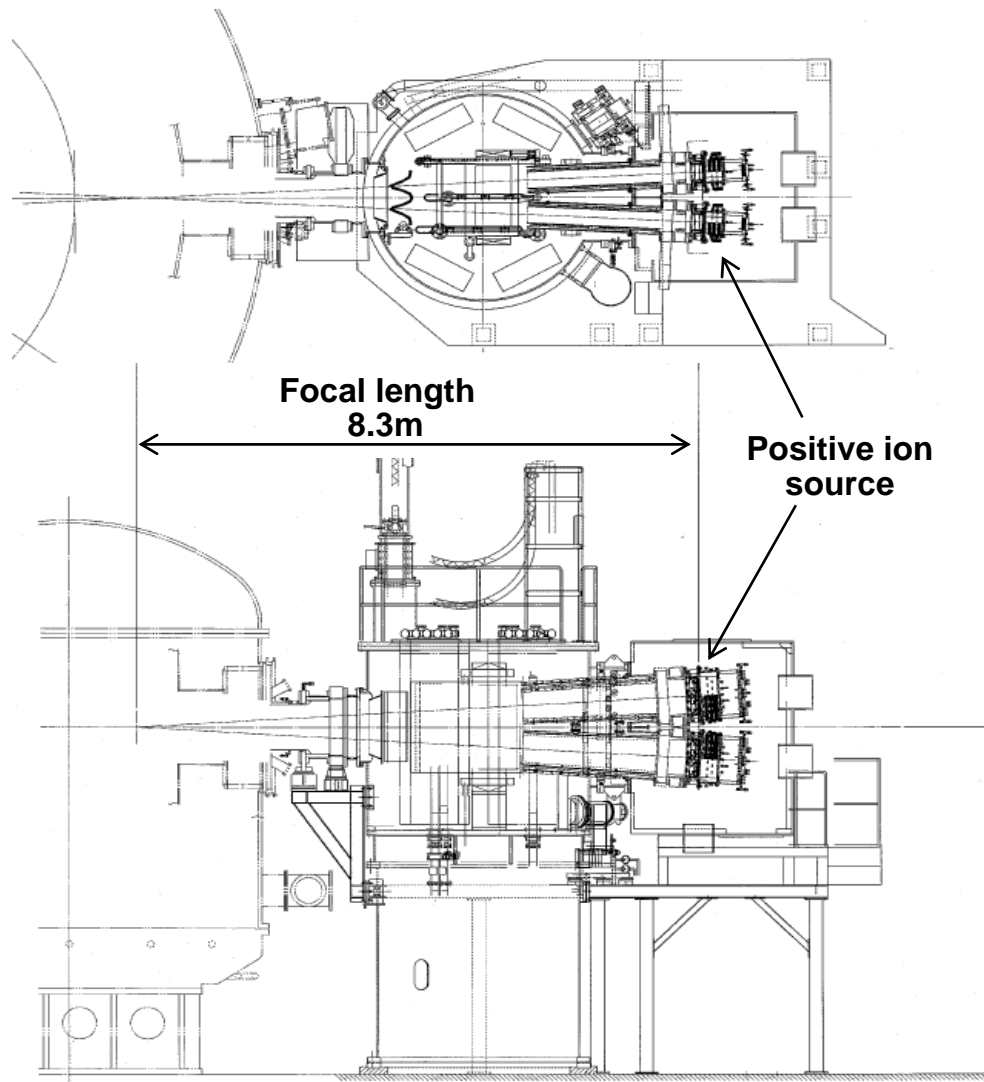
計測用の垂直入射ビームシステムBL4の平面図と立面図。
